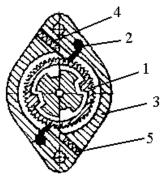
Поворотный механизм с двумя собачками в корпусе.
